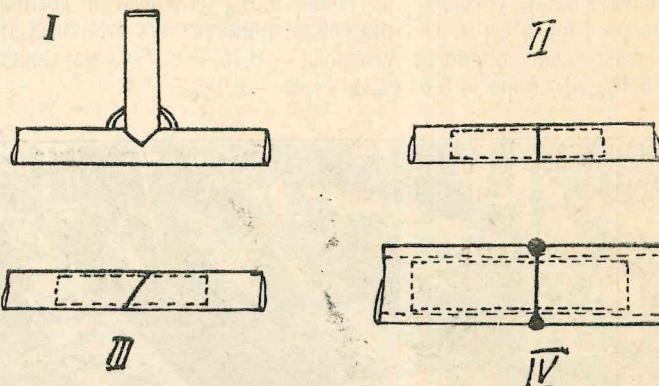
Типы свариваемых соединений: I — сварка труб под прямым углом с присоединением ушек; II — сварка двух труб одинакового диаметра, предназначенных для растягивающих усилий; III — труба, предназначенный для сжимающих усилий; IV — деталь сварки труб.
